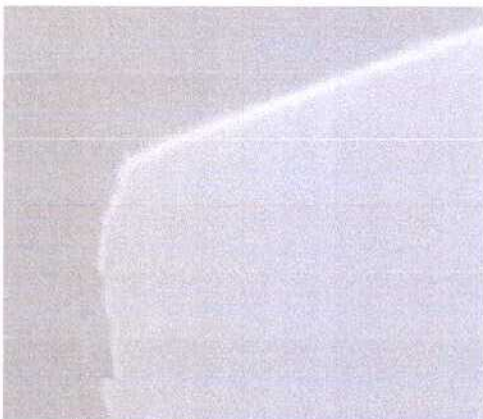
Zona defectuosa de la soldadura Al-SS producida por el contacto del extremo del pin con el SS. M.O.
